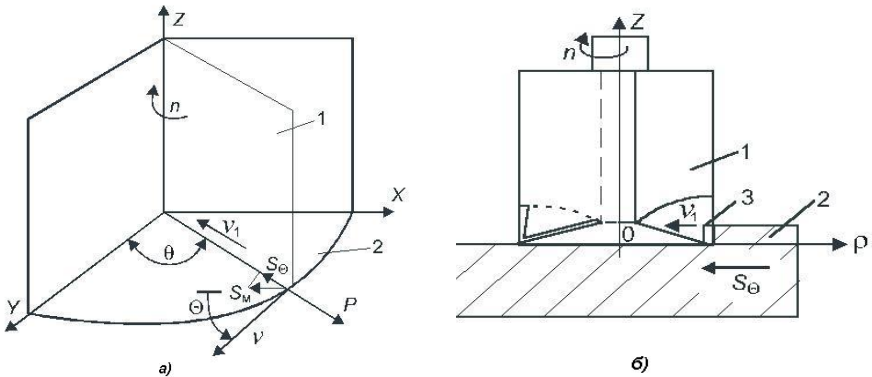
Принципиальная кинематическая схема фрезерования (а) и схема торцевого фрезерования в основной плоскости (б);
